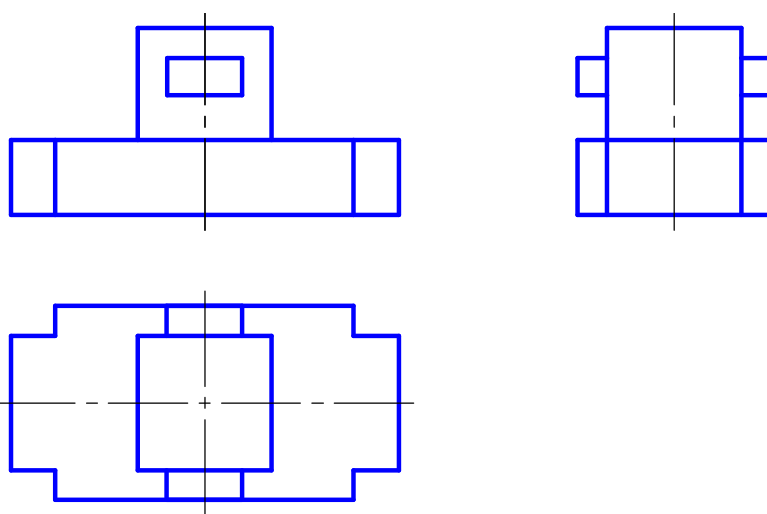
Чертеж детали по рис. 11, содержащий три вида: спереди, сверху и слева.
